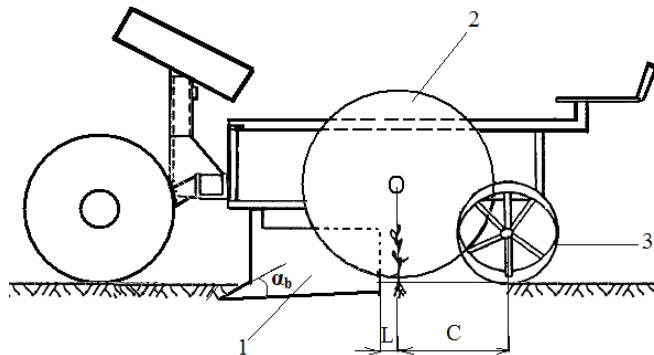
Poziția brăzdarului și a roților de tasare față de aparatul de plantare:
